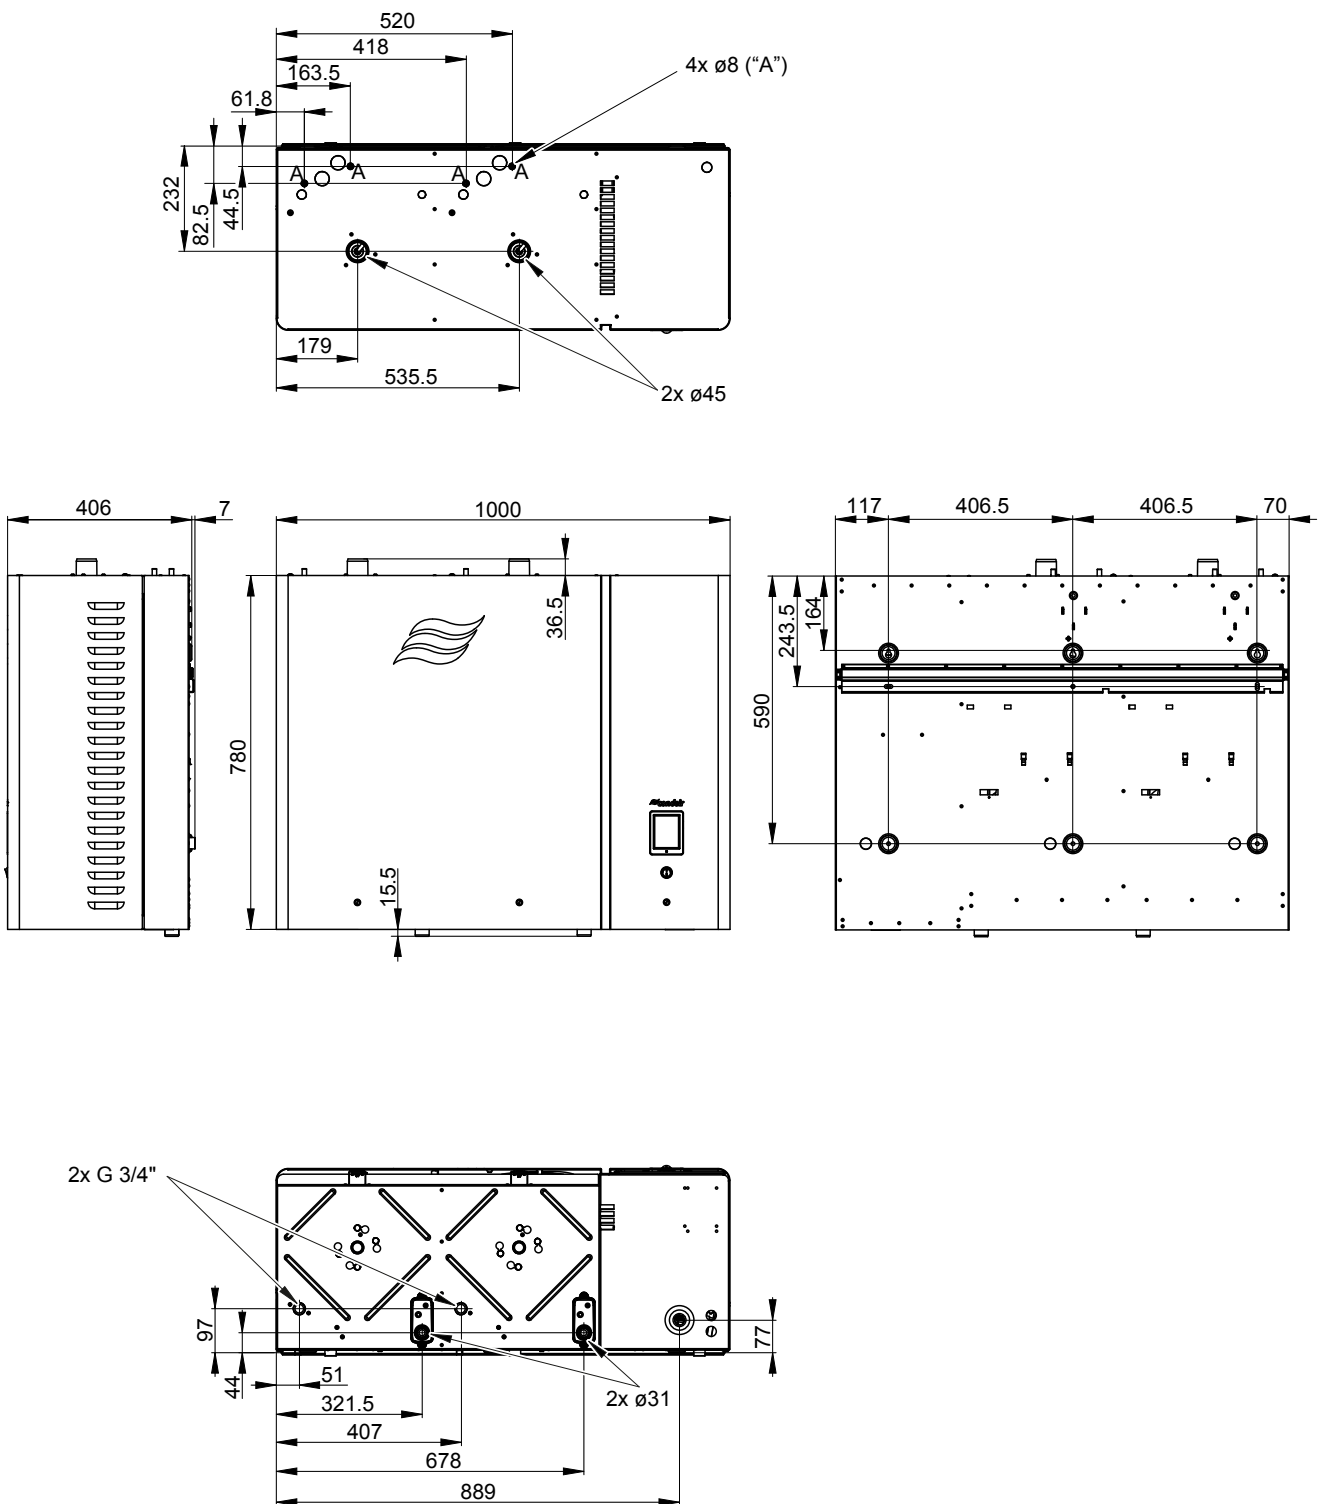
Figura de dimensiones Condair EL 50 - 90, tamaño de la carcasa "L" (dimensiones en mm)
